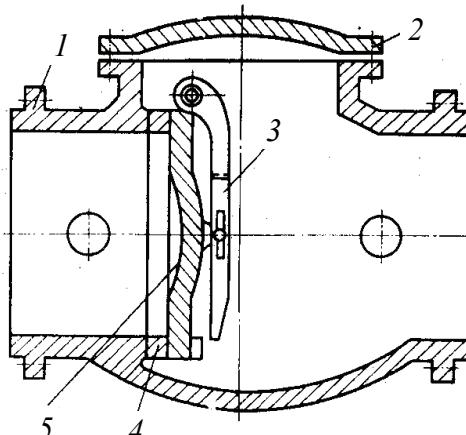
Схема устройства обратного клапана: 1 – корпус обратного клапана; 2 – крышка; 3 – рычаг; 4 – седло; 5 – тарелка
